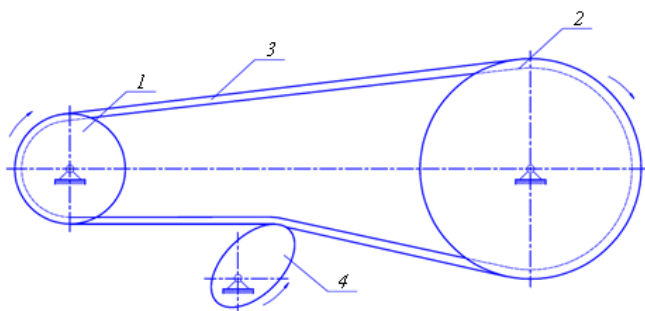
Схема ременной передачи с натяжным профилем кулачка
